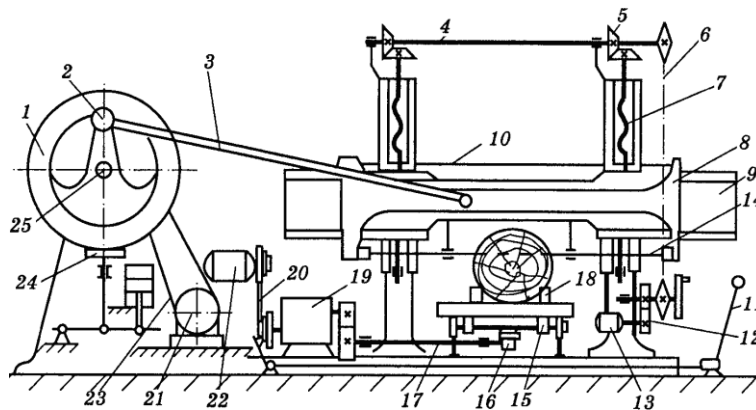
Схема горизонтальної пилорами: 1 – маховик; 2 – кривошипний палець; 3 – шатун; 4, 17 – вали; 5 – конічна зубчаста передача; 6 – ланцюгова передача; 7 – гвинт переміщення супорта; 8 – пилкова рамка; 9 – супорт; 10 – струна; 11 – важіль переключення швидкості подачі; 12 – зубчаста передача; 13 – електродвигун приводу вертикального переміщення супорта; 14 – пилка; 15 – візок; 16 – шестірня з рейкою; 18 – спеціальний гачок; 19 – редуктор; 20 – пасова передача; 21 – електродвигун приводу головного вала; 22 – електродвигун приводу подачі; 23 – клинопасова передача; 24 – гальмо; 25 – головний вал
